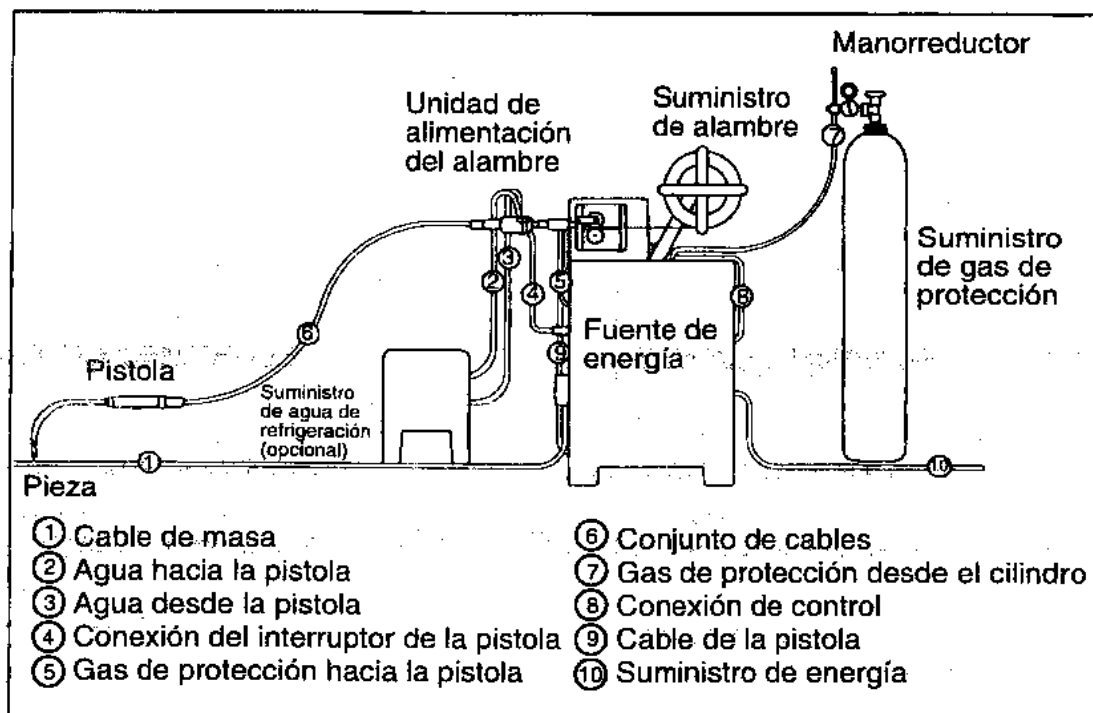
EQUIPO PARA EL SOLDEO MIG/MAG
